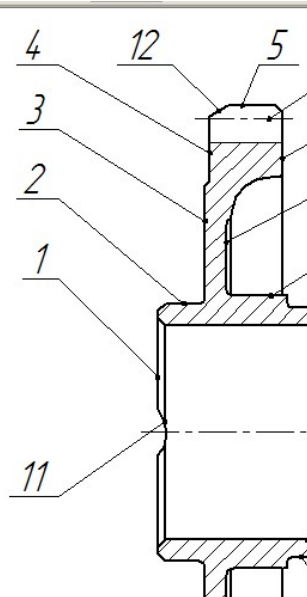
Ескіз деталі з нумерацією поверхонь:
